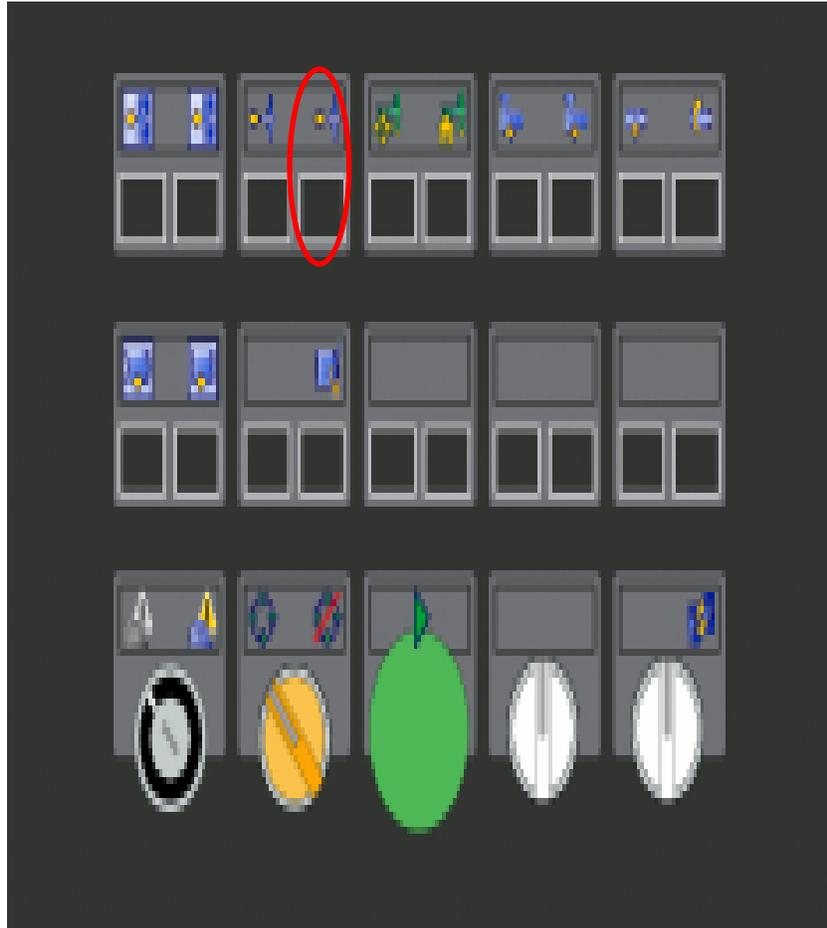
(operator manual machine duo 7050/1900 WP US ENGEL, 2013)
